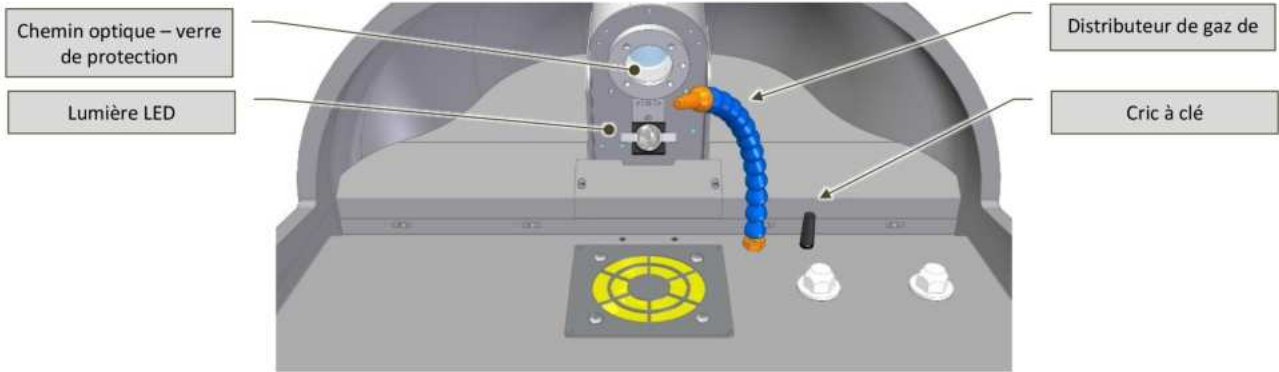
Chemin optique – vue depuis la chambre de soudage
